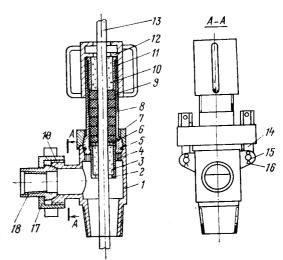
Сальник устьевой СУС1-73-31: I — тройник; 2 — втулка нижняя; 3 — вкладыш; 4 — стопор; 5 — кольцо уплотнительное; 6 — манжетодержатель; 7 — крышка шаровая; 8 — уплотнительная набивка; 9 — головка шаровая; 10 — вкладыш; 11 — грундбукса; 12 — крышка головки; 13 — шток; 14 — болт откидной; 15 — палец; 16 — шплинт; 17 — гайка накидная; 18 — ниппель; 19 — наконечик
